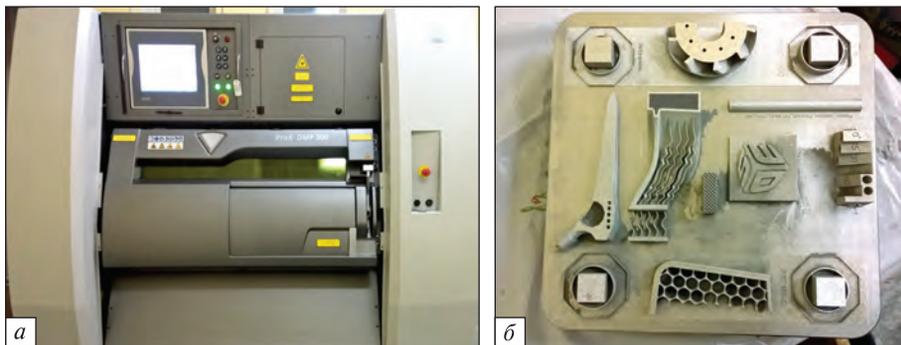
Внешний вид 3D-принтера ProX DMP 300 (а), рабочая платформа принтера с образцами деталей построенных деталей (б)
